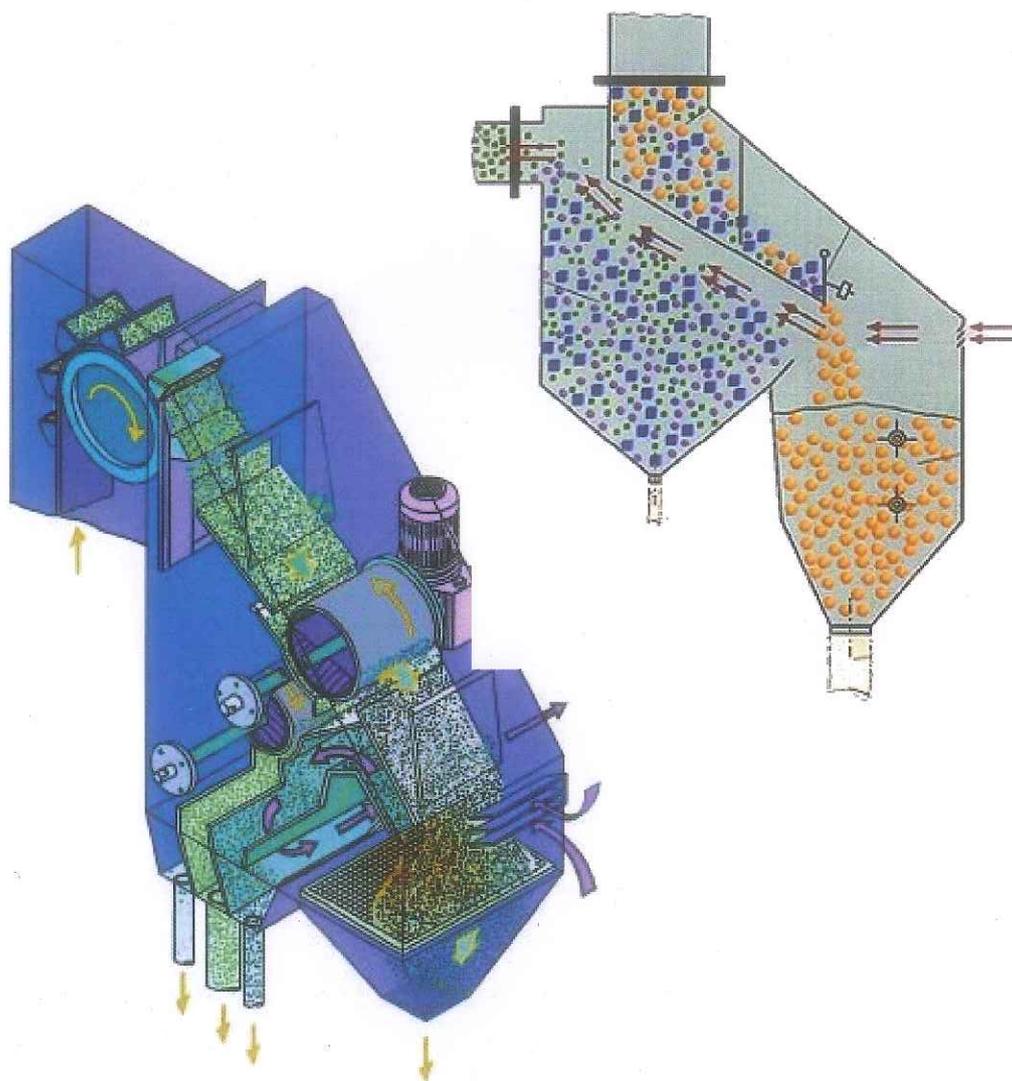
Элеватор и Сепаратор (стрелки показывают направление движения стальной дроби)
